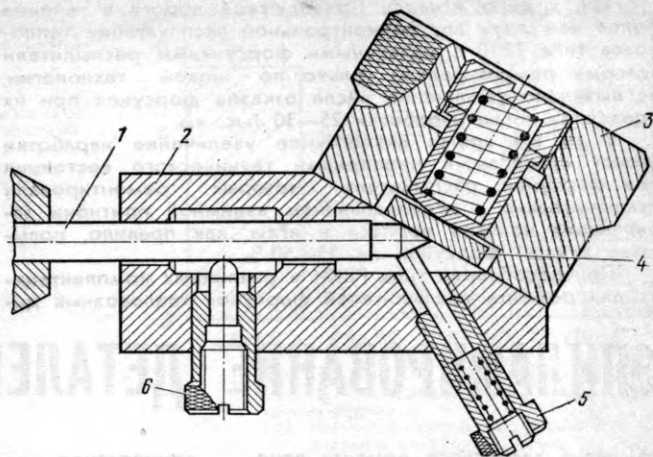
Приспособление для правки конусных притиров: 1 — притир; 2 — корпус приспособления; 3 — прижимное устройство; 4 — доводочный инструмент; 5 — радиально-осевой упор; 6 — регулируемый радиальный упор
